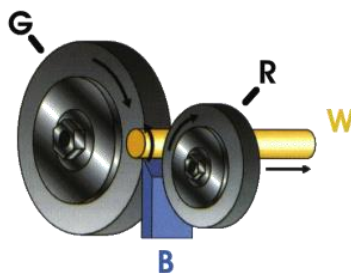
Rectificado sin centros. Fuente: Rectyafil
